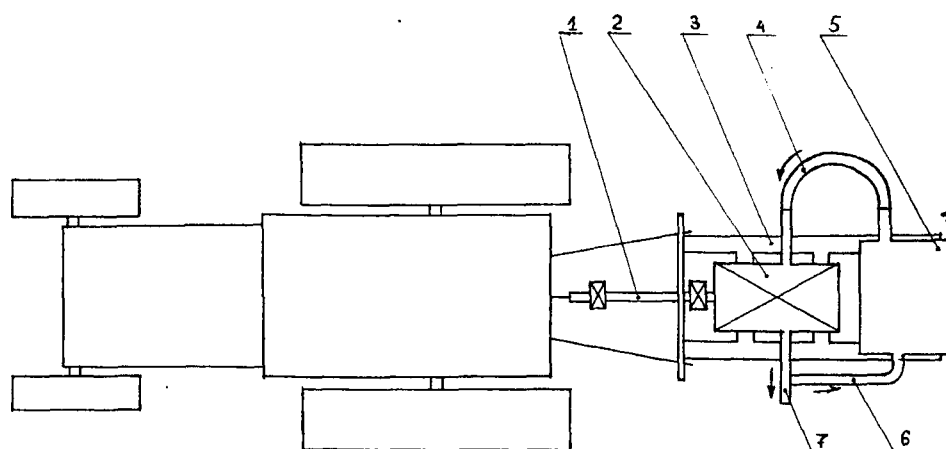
1 - карданный вал; 2 - поршневой насос; 3 - рама; 4 - заборный патрубок; 5 - емкость; 6, 7 - патрубки.
